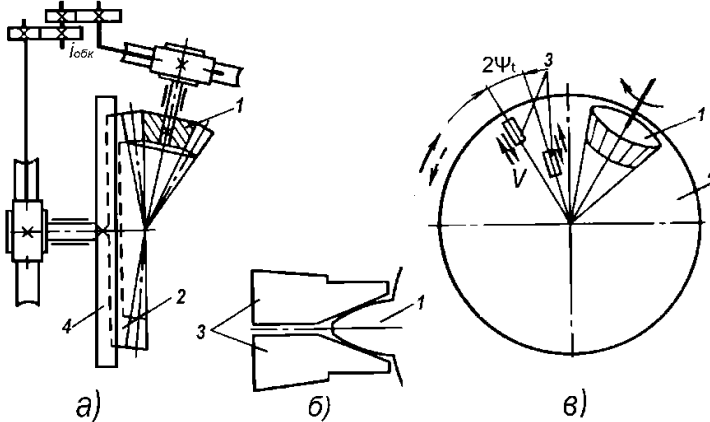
Схема нарізування конічних зубчастих коліс двома різцями
